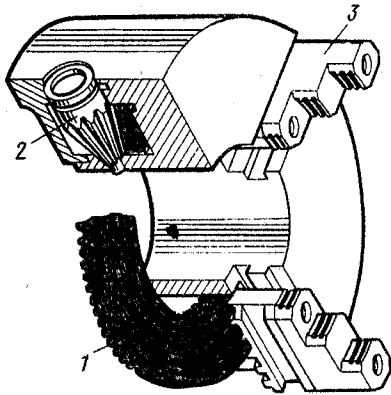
Трехкулачковый патрон внутришлифовального станка
